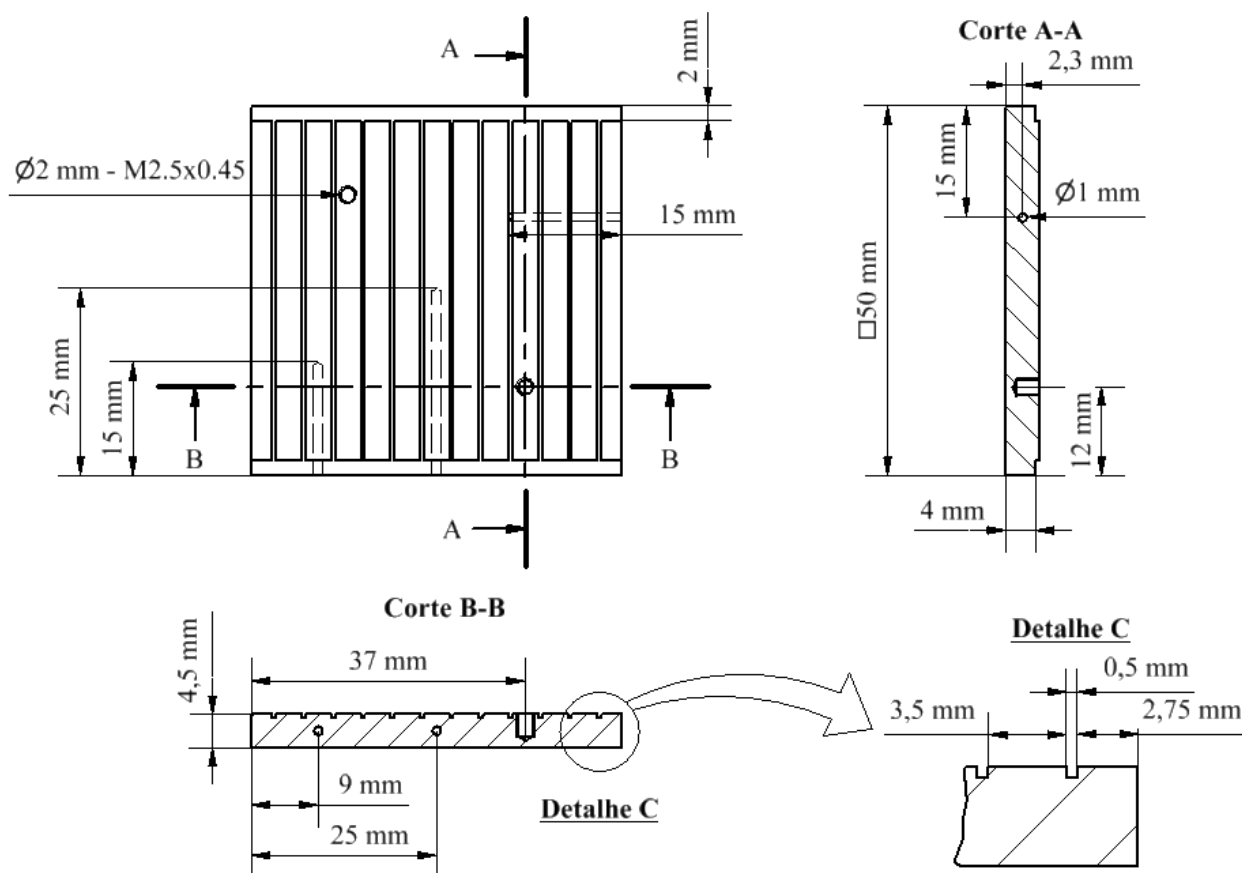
Dimensões e detalhes da placa de alumínio.
